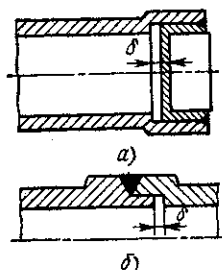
Допуски на расширение материала при сварке:
